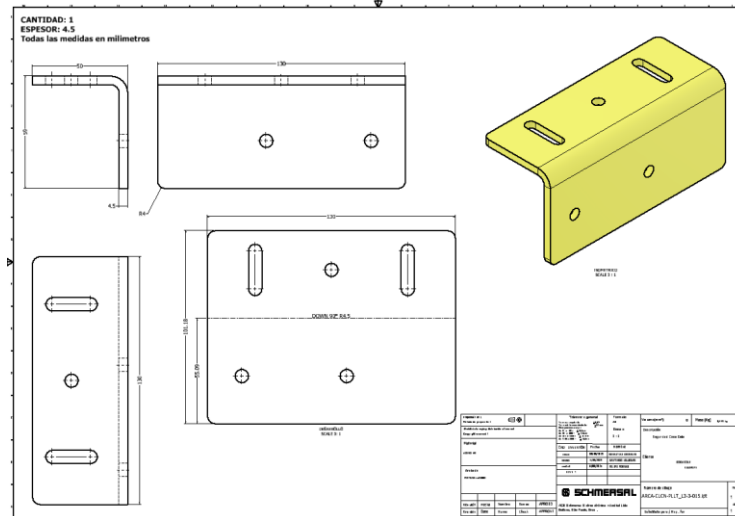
Lamina a fabricar en corte laser que será soporte de actuador AZM300
